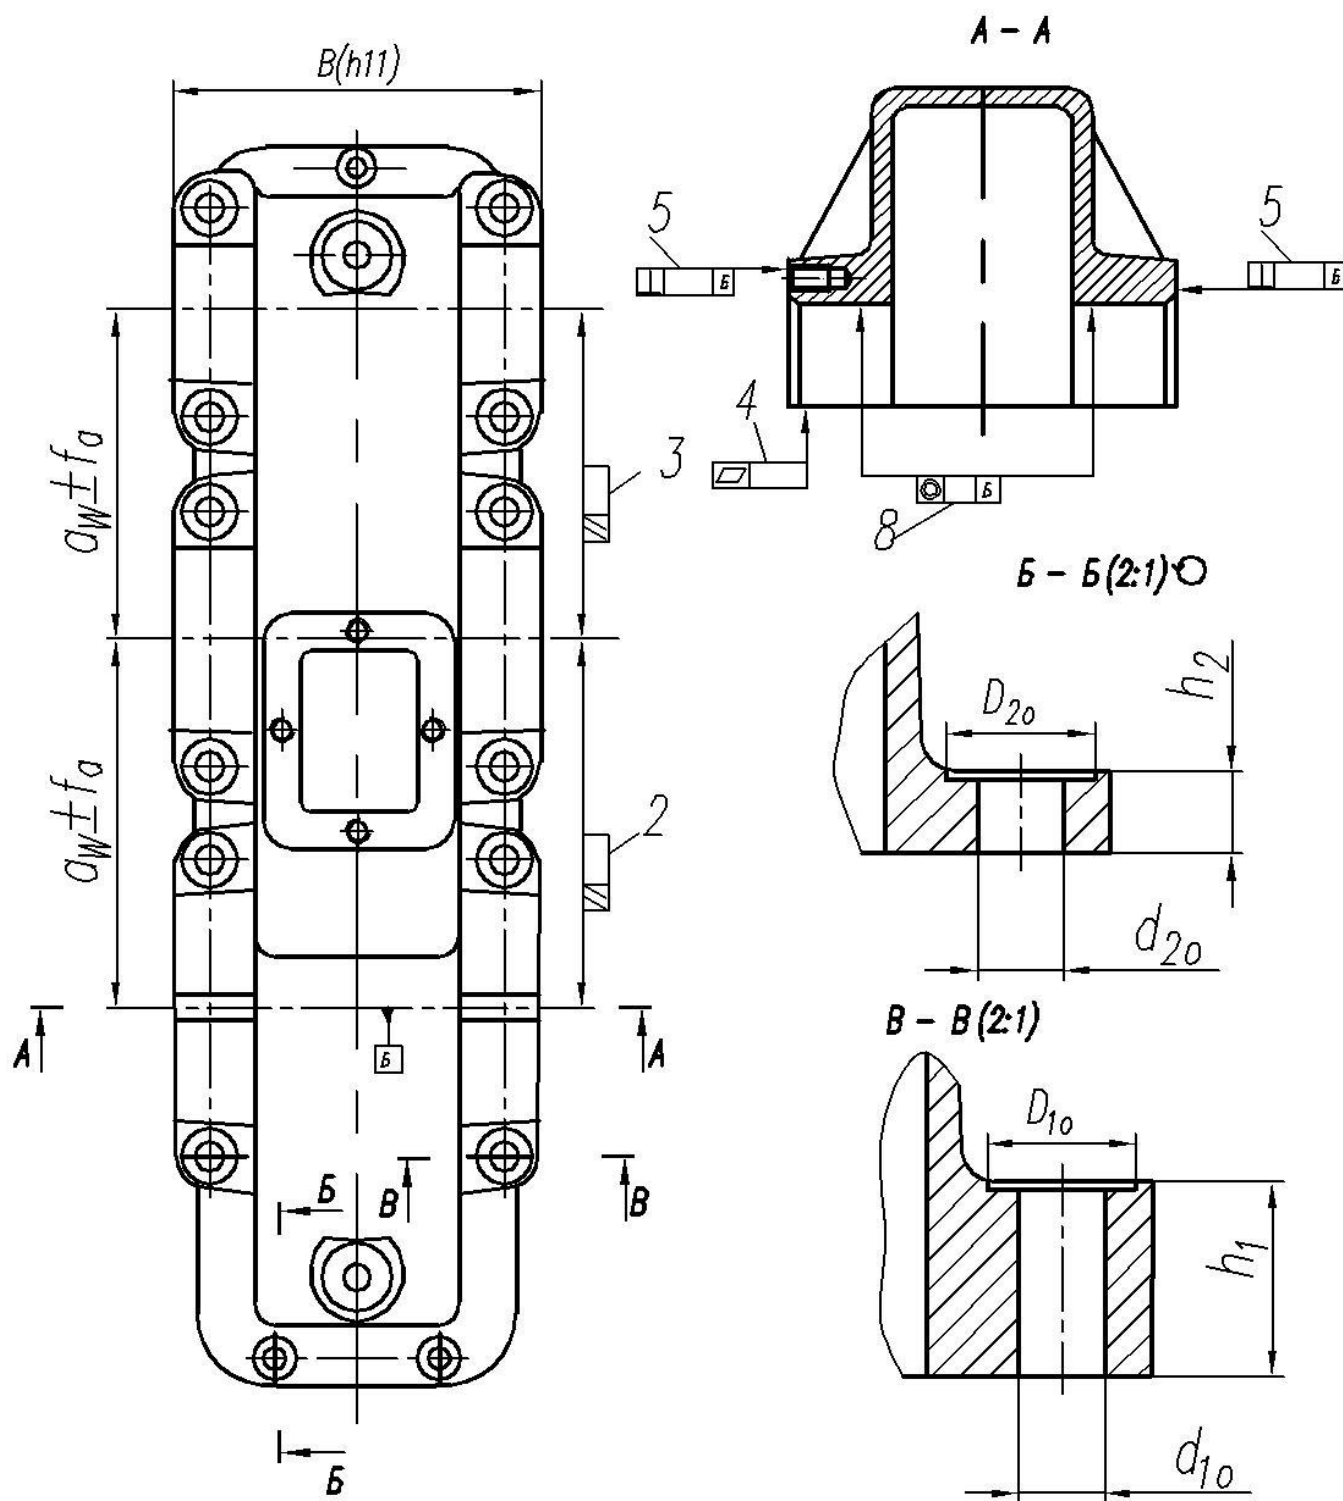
Размещение обозначений допусков форм и расположения поверхностей на чертеже крышки корпуса
